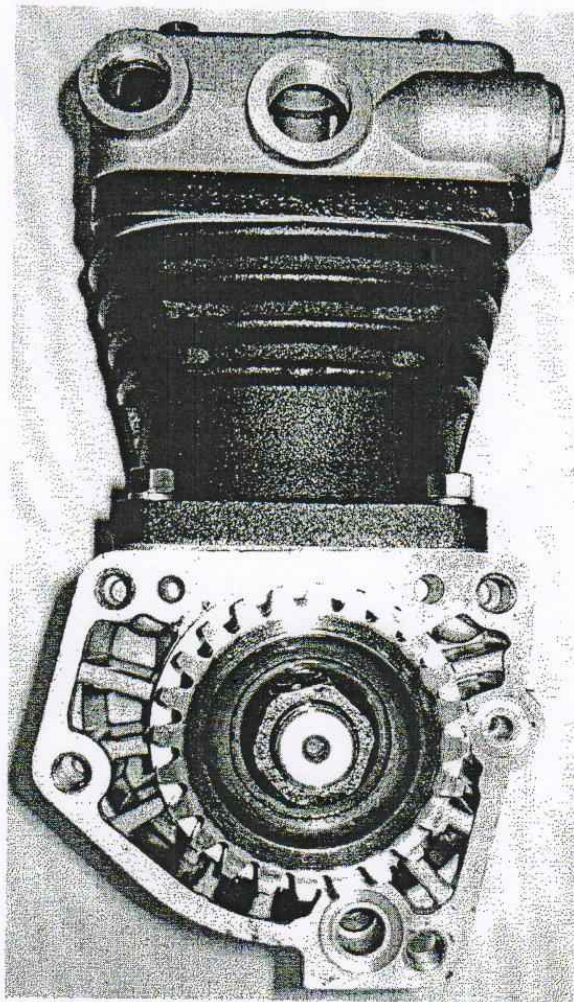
Общий вид одноцилиндрового автомобильного компрессора, изд. 133.3509015.
